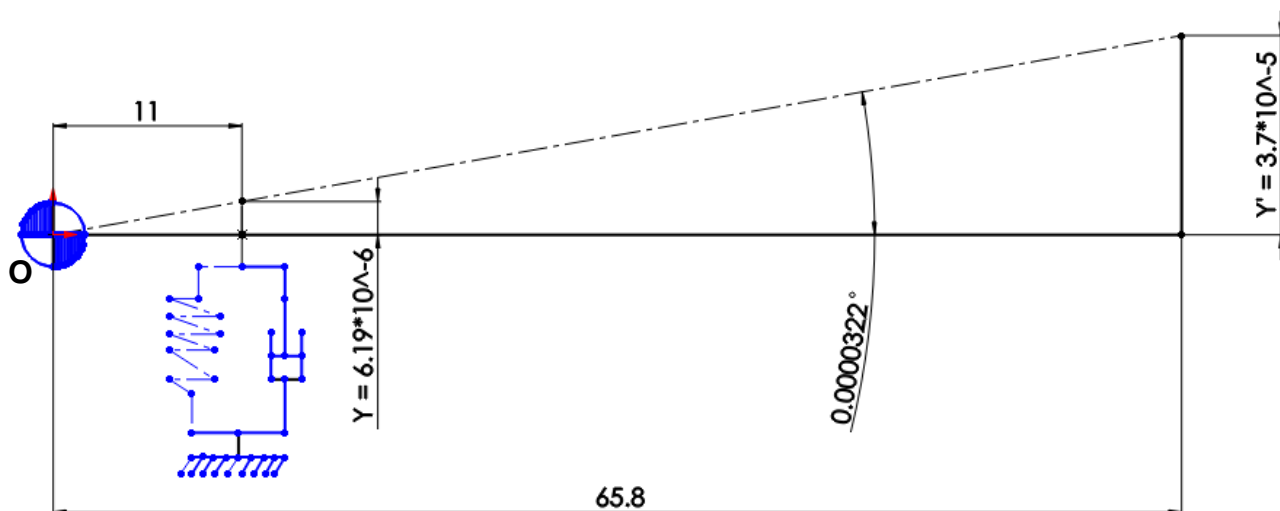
Угловое и линейное перемещение корпуса редуктора.
